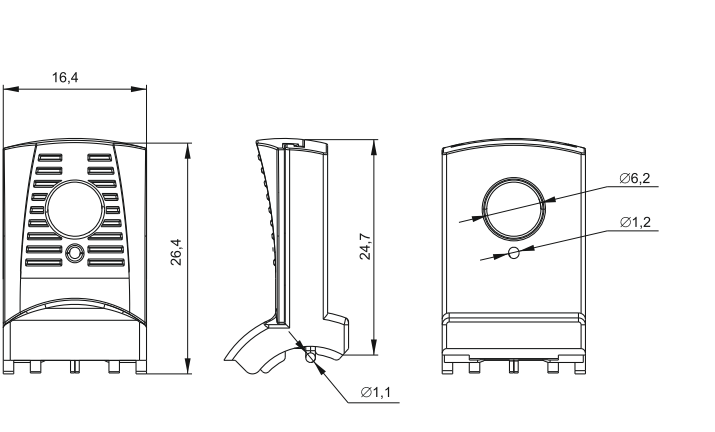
Габаритные размеры блокировки / Figure 1 – Overall dimensions of the interlock
